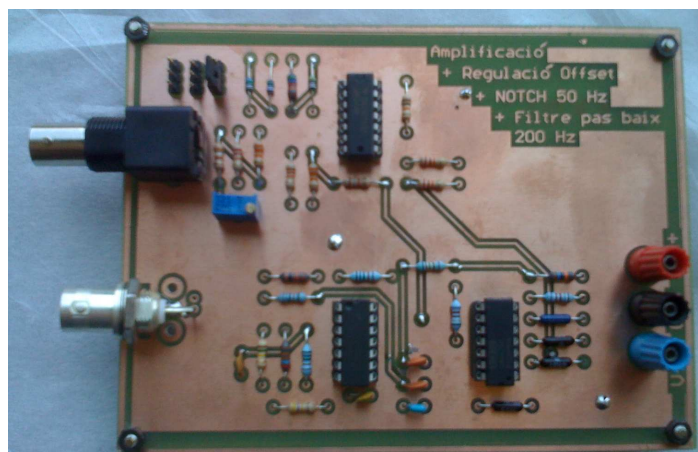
Revelat de la placa PCB vista per la cara Top.
